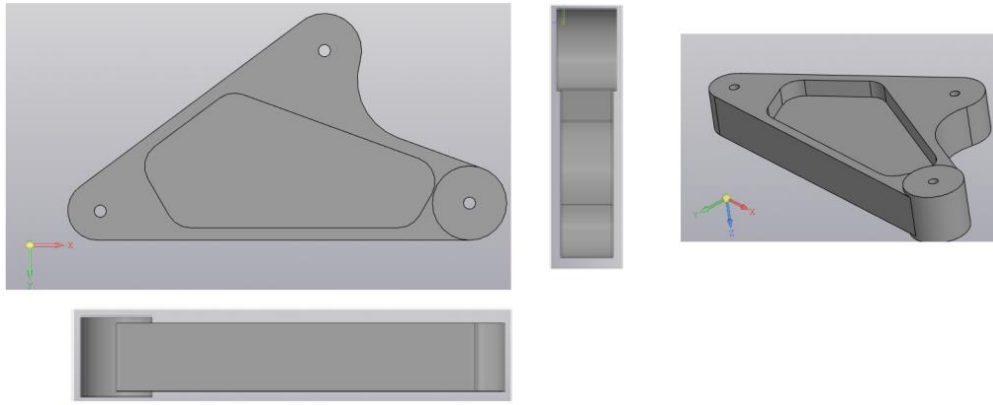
Комп'ютерна 3D-модель заготовки деталі «Качалка»
